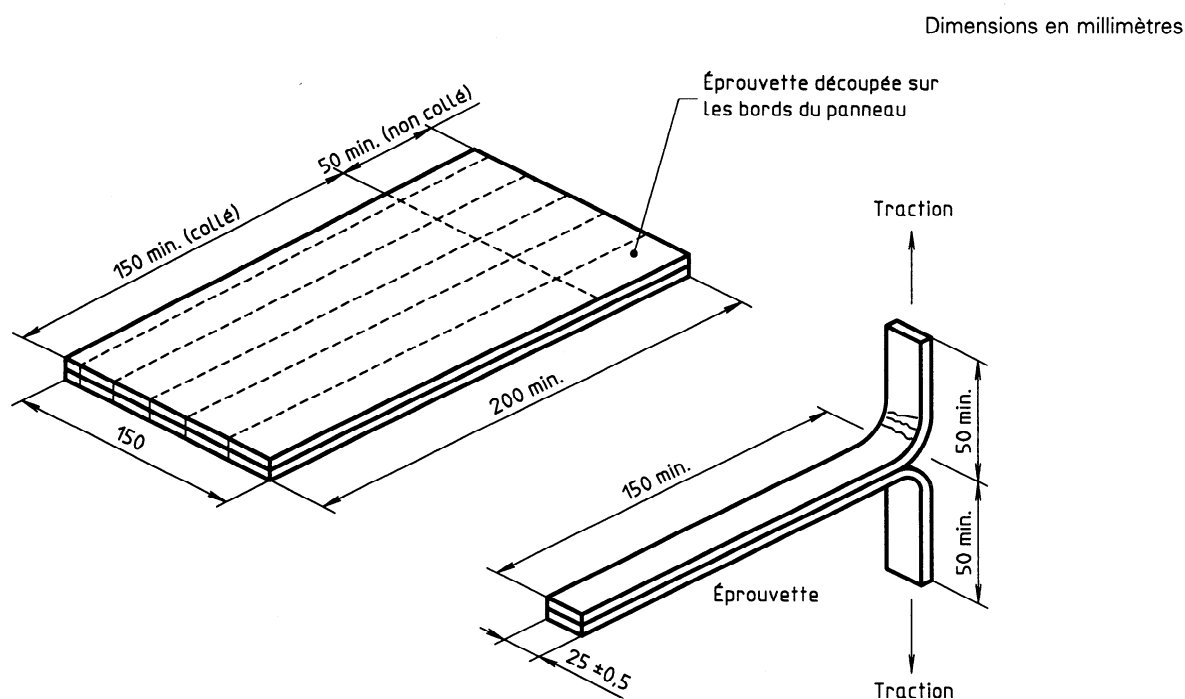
Panneau avant découpe et éprouvette individuelle après découpe
